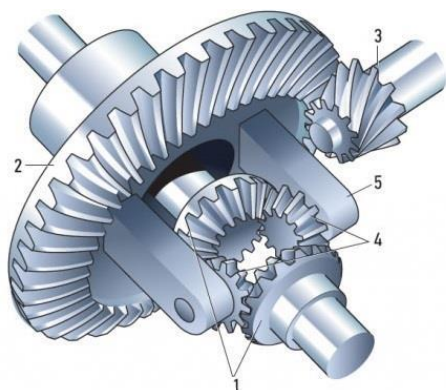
Устройство конического дифференциала: 1 – шестерни полуосей; 2 – ведомая шестерня главной передачи; 3 – ведущая шестерня главной передачи; 4 – сателлиты; 5 – корпус
